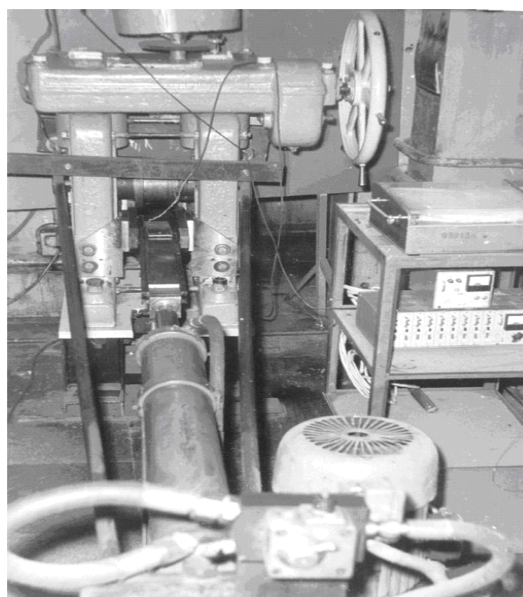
Установка для периодической прокатки полосовых заготовок
